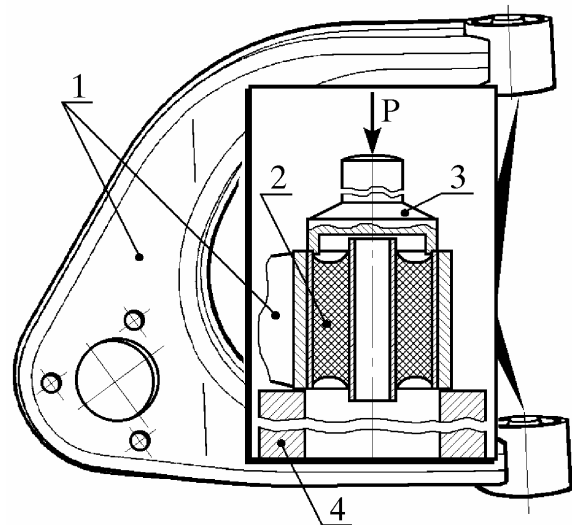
Выпрессовка сайлентблоков из отверстий верхнего рычага:
